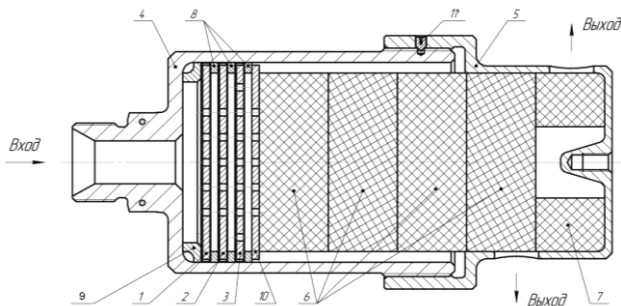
Конструкция глушителя шума выхлопа испытательного стенда
